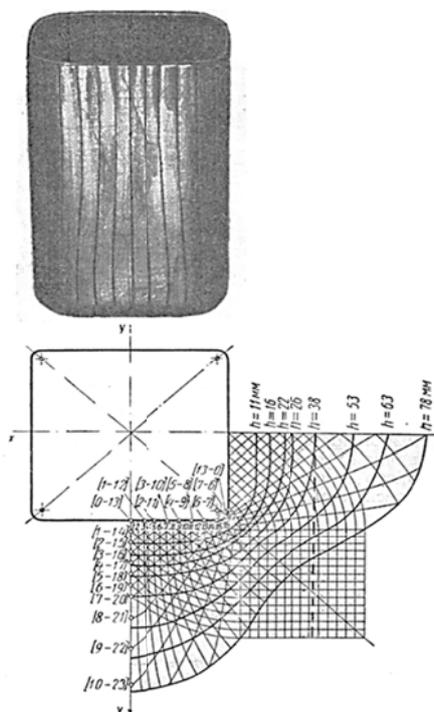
Размеры и форма оптимальных заготовок для вытяжки квадратных коробок различной высоты и деталь, полученная из оптимальной заготовки ($H/B=0,95$) [6]
